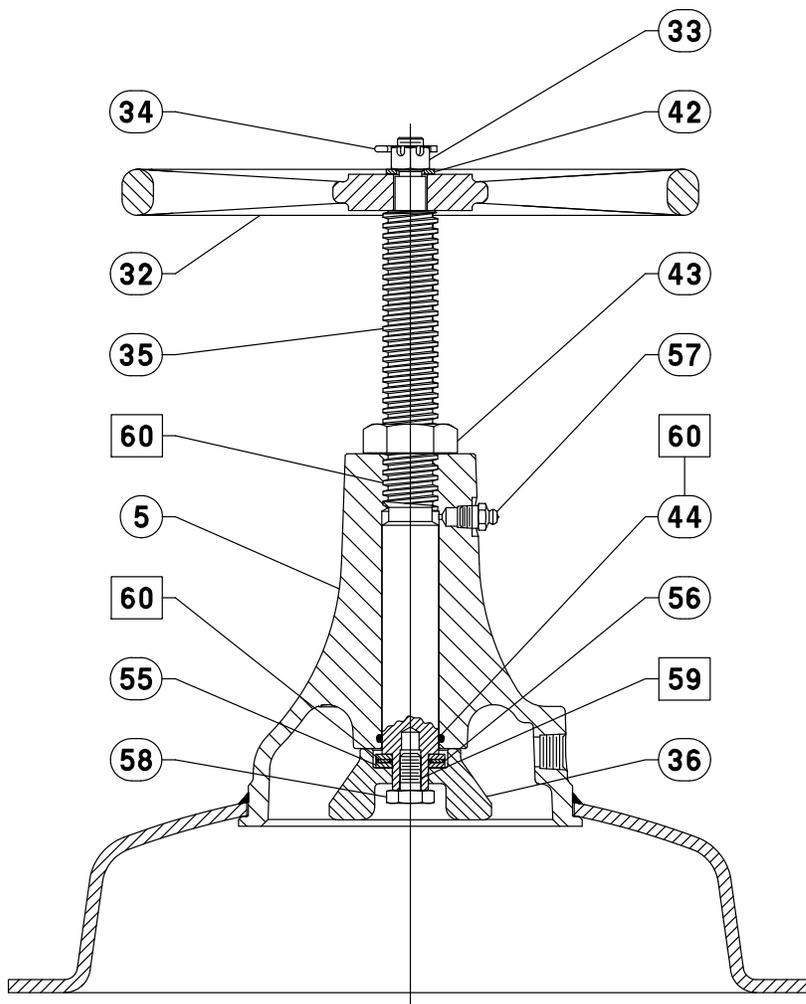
Gruppo del volante 2052 di dimensione 1 Fisher
